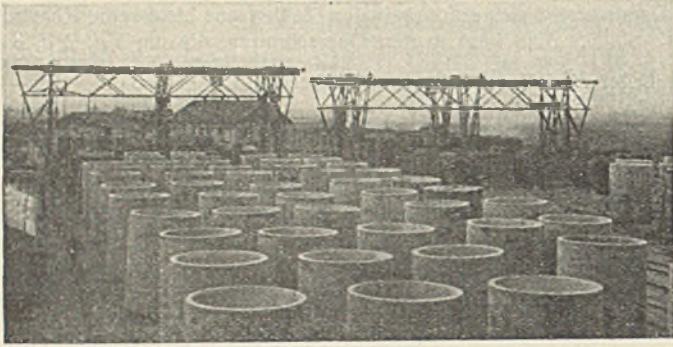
Lagerplatz der Schleuderrohrfabrik bei Unterföhring der Züblin & Cie. A.-G.
